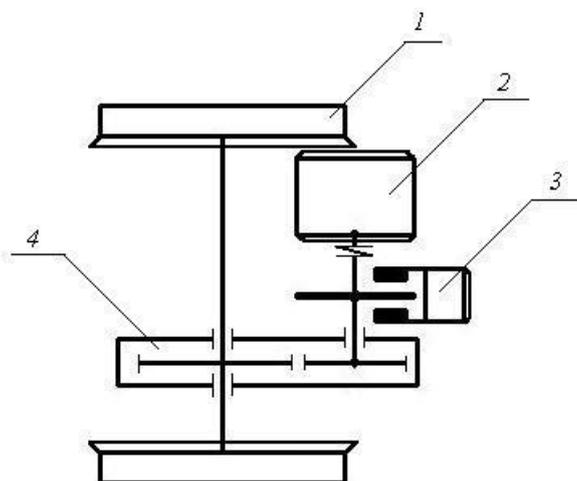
Привод колесной пары. 1- колеса; 2- электродвигатель; 3 – дисковый тормоз; 4 – редуктор.
